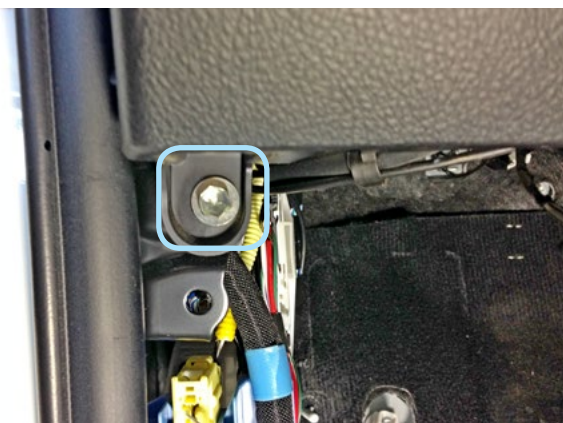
Болт крепления накладки под рулевой колонкой слева
